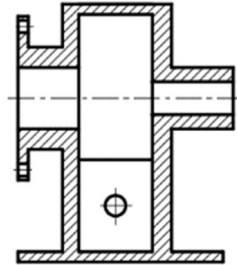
Кресленик фронтального розрізу А-А корпусу
